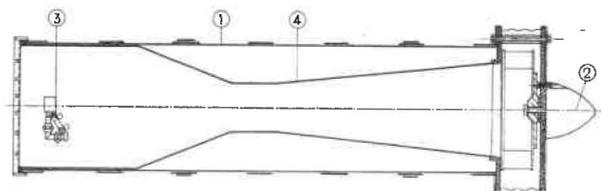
Vue en coupe du dépoussiéreur léger Samia type DV3.
